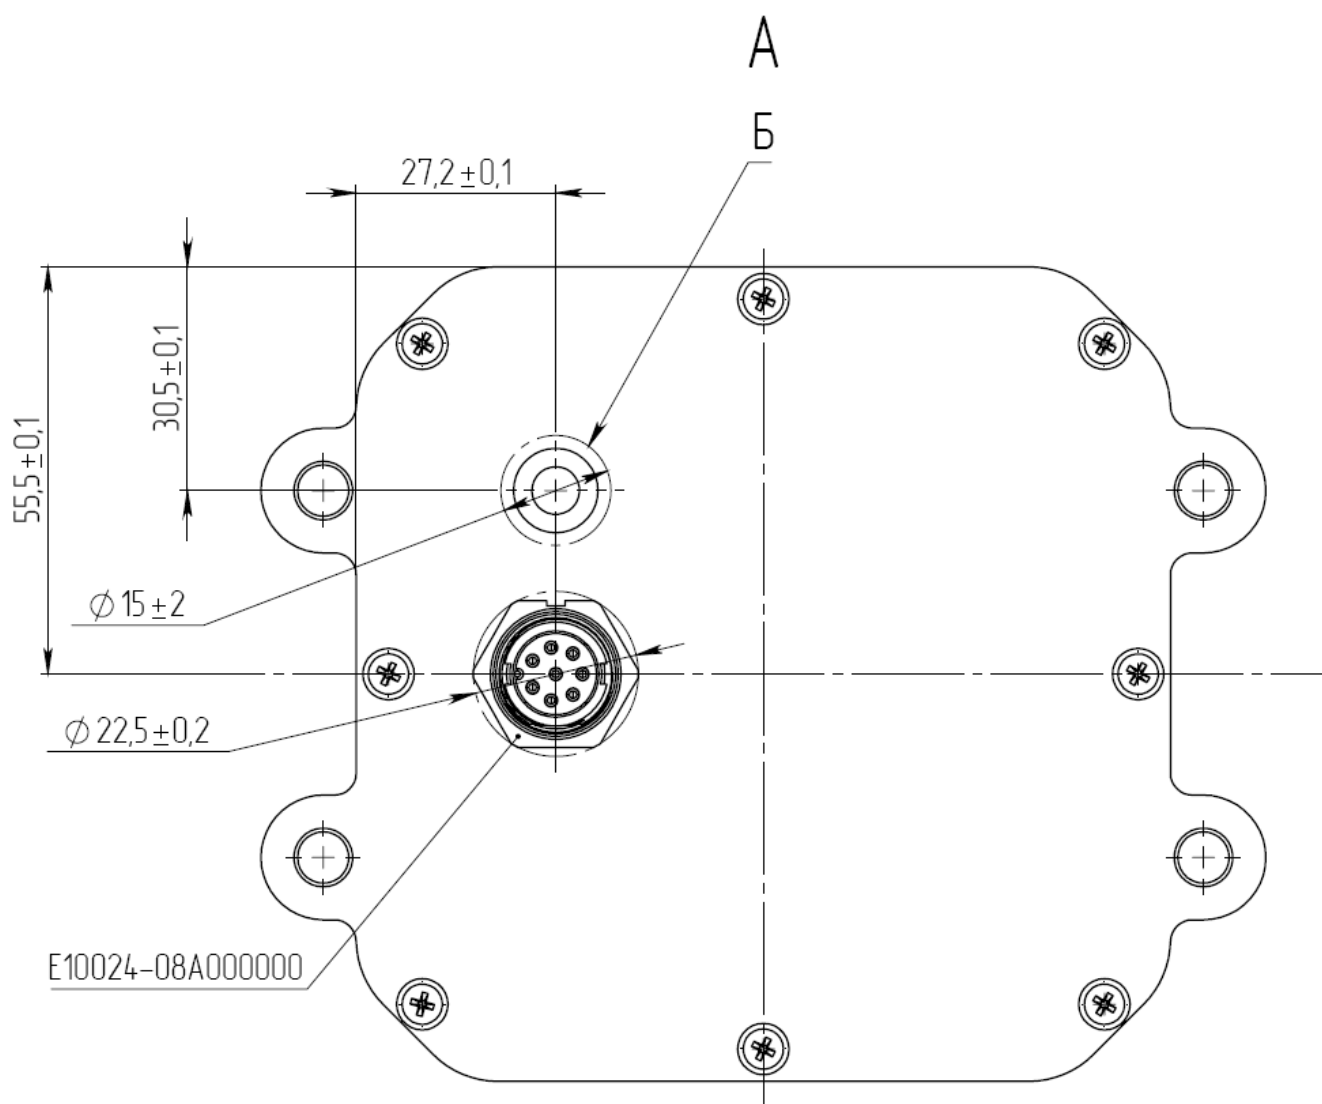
Габаритные размеры исполнения изделия ТСКЯ.466369.007-02, маркировка, расположение отверстий для крепления (лист 1 из 2)
